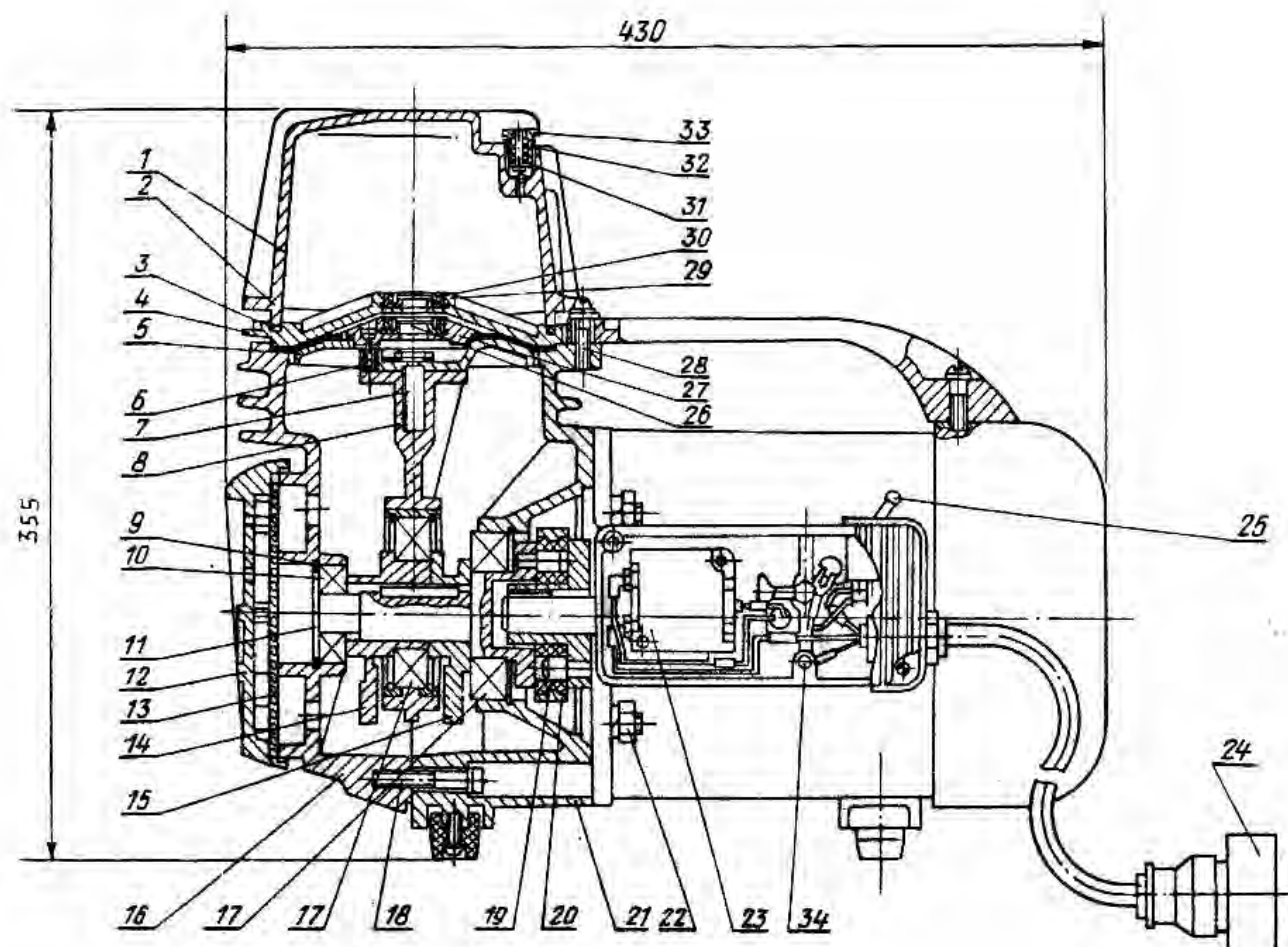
Компрессор диафрагменный СО-45Б (в разрезе):
